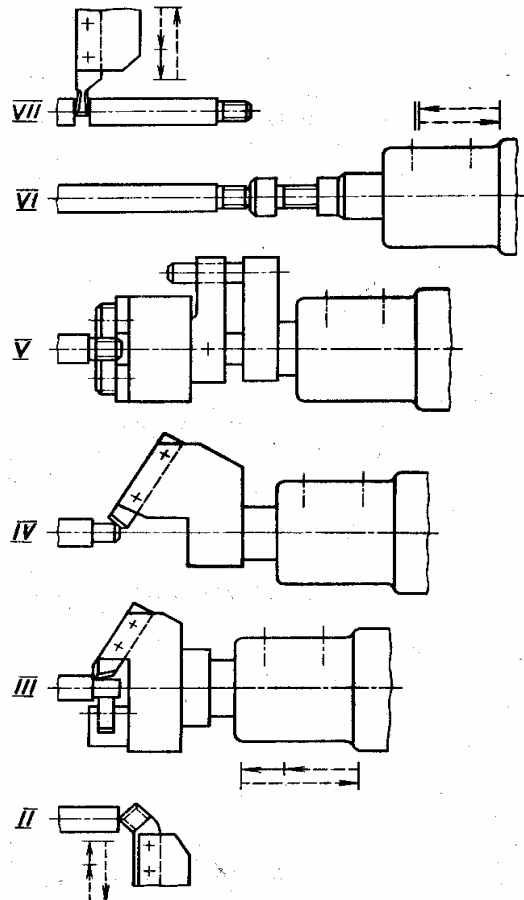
Схеми обробки пальця з пруткового матеріалу: I – звільнення прутка, подача його до упора та фіксація з малим вильотом (не показаний) II – підрізання торця; III – обточування циліндричного ступеня під різьбу; IV – зняття фаски; V – нарізання різьби; VI – подача прутка до упора на довжину деталі то його закріплення; VII – відрізання деталі
